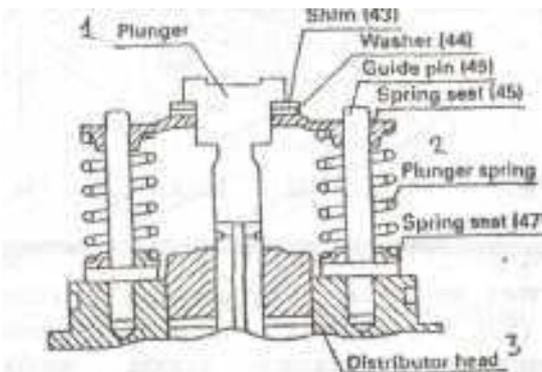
Головка насоса в сборе с плунжером 1-плунжер, 2-пружина плунжера, 3-головка насоса, (43)- прокладка, (44)-шайба, (45) и (47) -седла пружины, (49)- направляющий стержень
